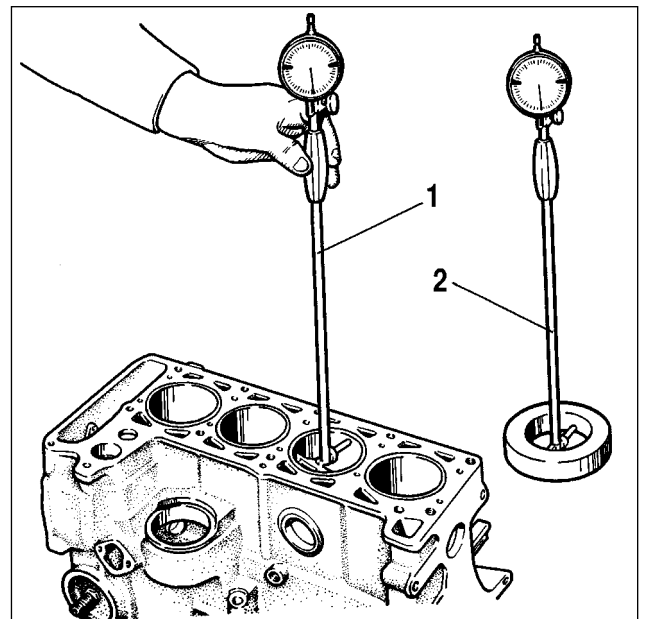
Messung von Zylindern mit Innenmeßgerät:
